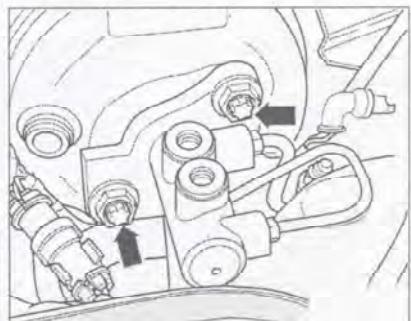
Отверните болты (стрелки) главного тормозного цилиндра.
